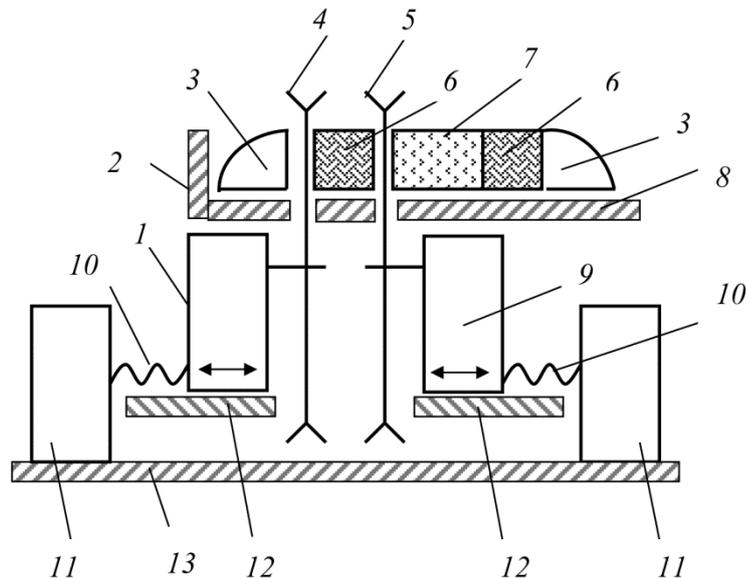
Схема переработки древесины с ядровой гнилью на обрезном станке: 1, 9 – электродвигатели; 2 – боковые направляющие; 3 – обзоленные кромки обрезаемого пиломатериала; 4, 5 – дисковые пилы для выпиливания обзоленной кромки и здоровой древесины; 6 – полосы здоровой древесины; 7 – ядровая гниль; 8 – горизонтальные направляющие; 10 – винтовая подача; 11 – устройства для смещения электродвигателей; 12 – направляющие; 13 – станина
